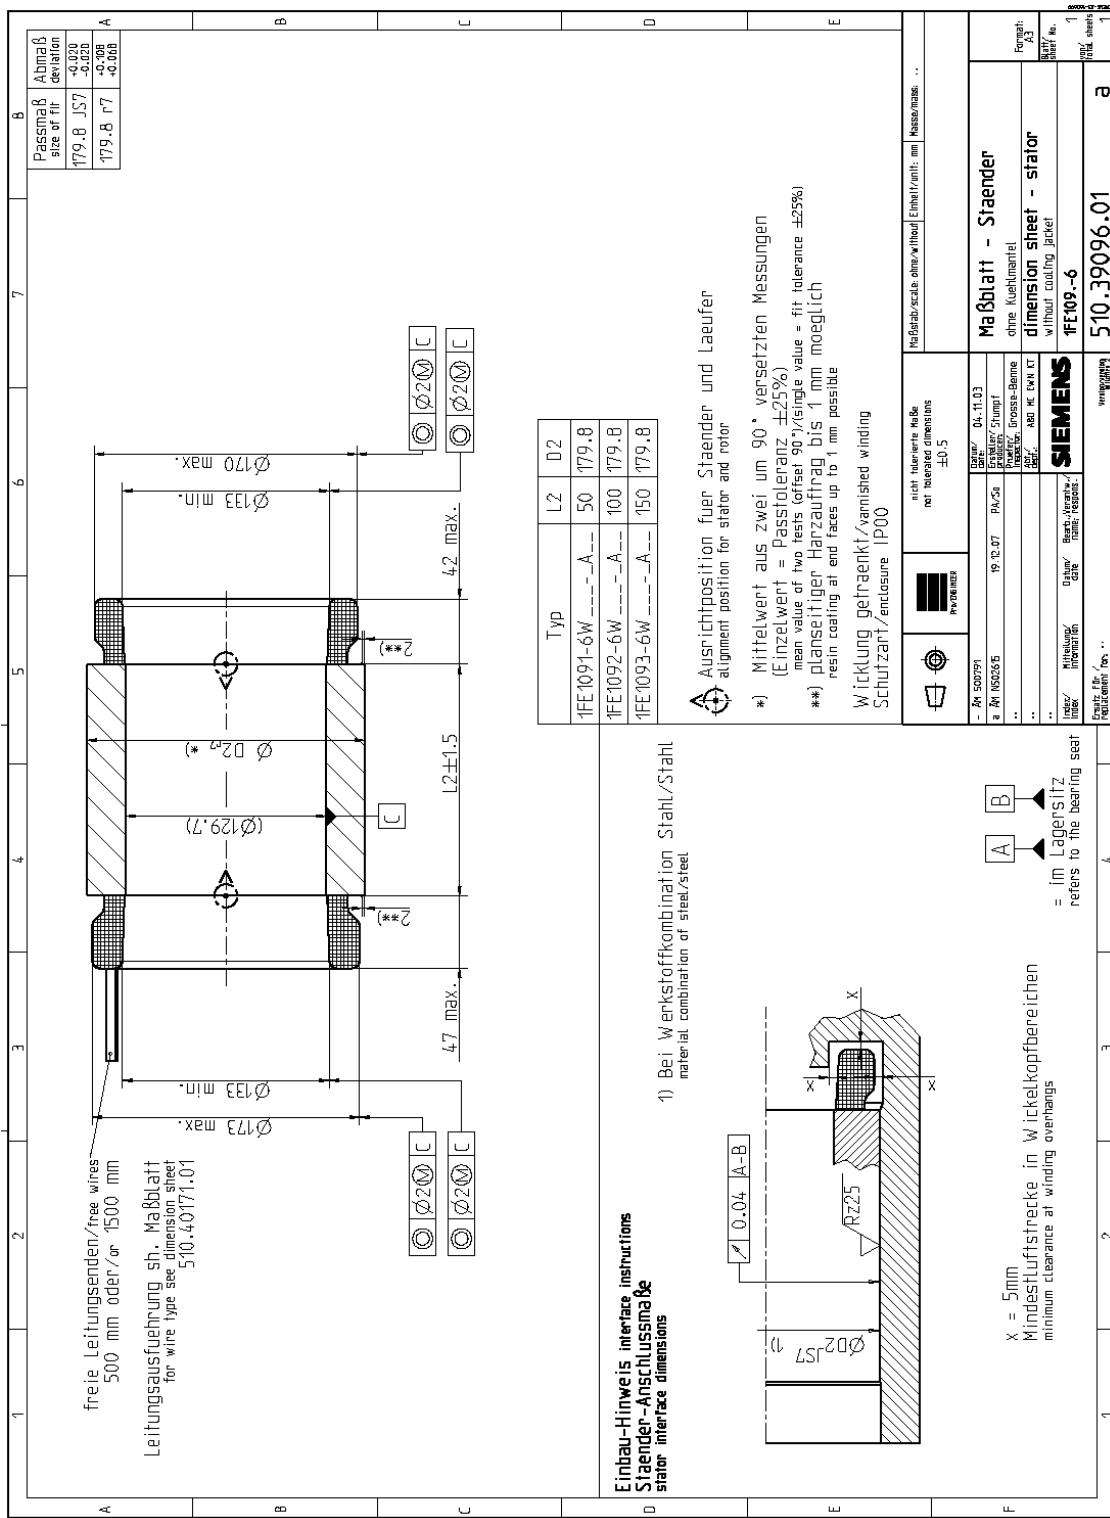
1FE109□-6, Ständer ohne Kühlmantel
